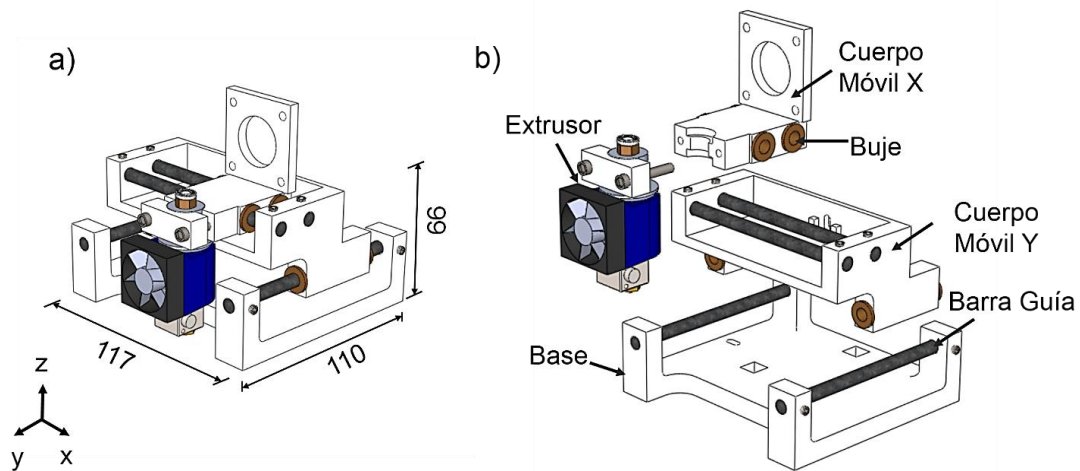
Diseño final chasis parte impresora considerando un sistema motriz engranaje cremallera (a) dimensiones generales en milímetros del sistema (b) extrusionado del sistema donde se indican las principales partes.
